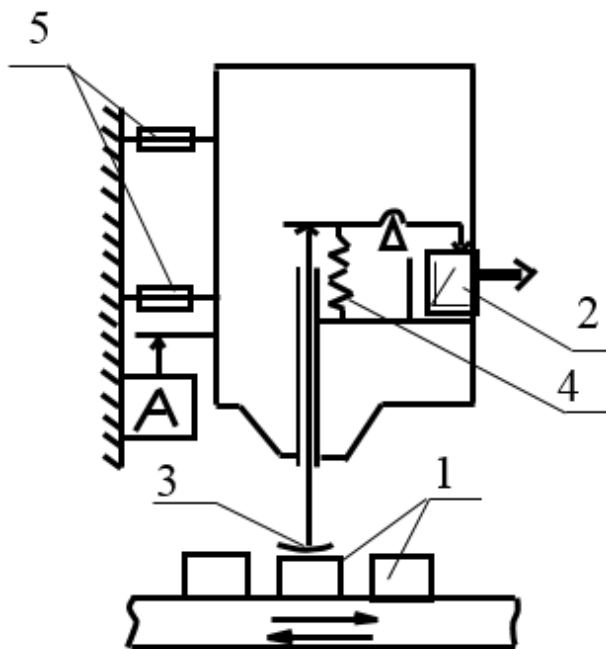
Вимірювальний пристрій для контролю висоти деталей
